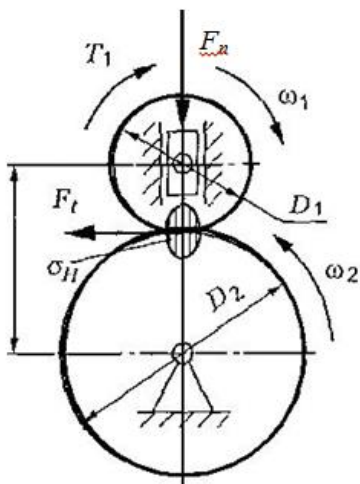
розрахункова схема циліндричної фрикційної передачі
